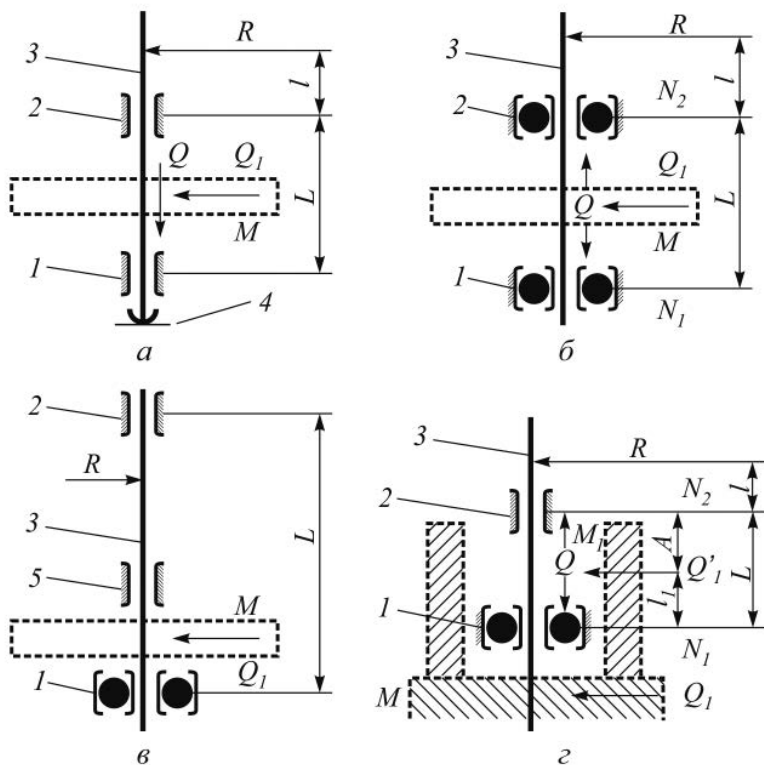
Схеми установки опор обертання приводних валів: а, б – двоопорна балка, в – триопорна балка, з – з консольним розташуванням опор (1, 2, 5 – опори, 3 – вал, 4 – посадочна базова поверхня корпусу)
